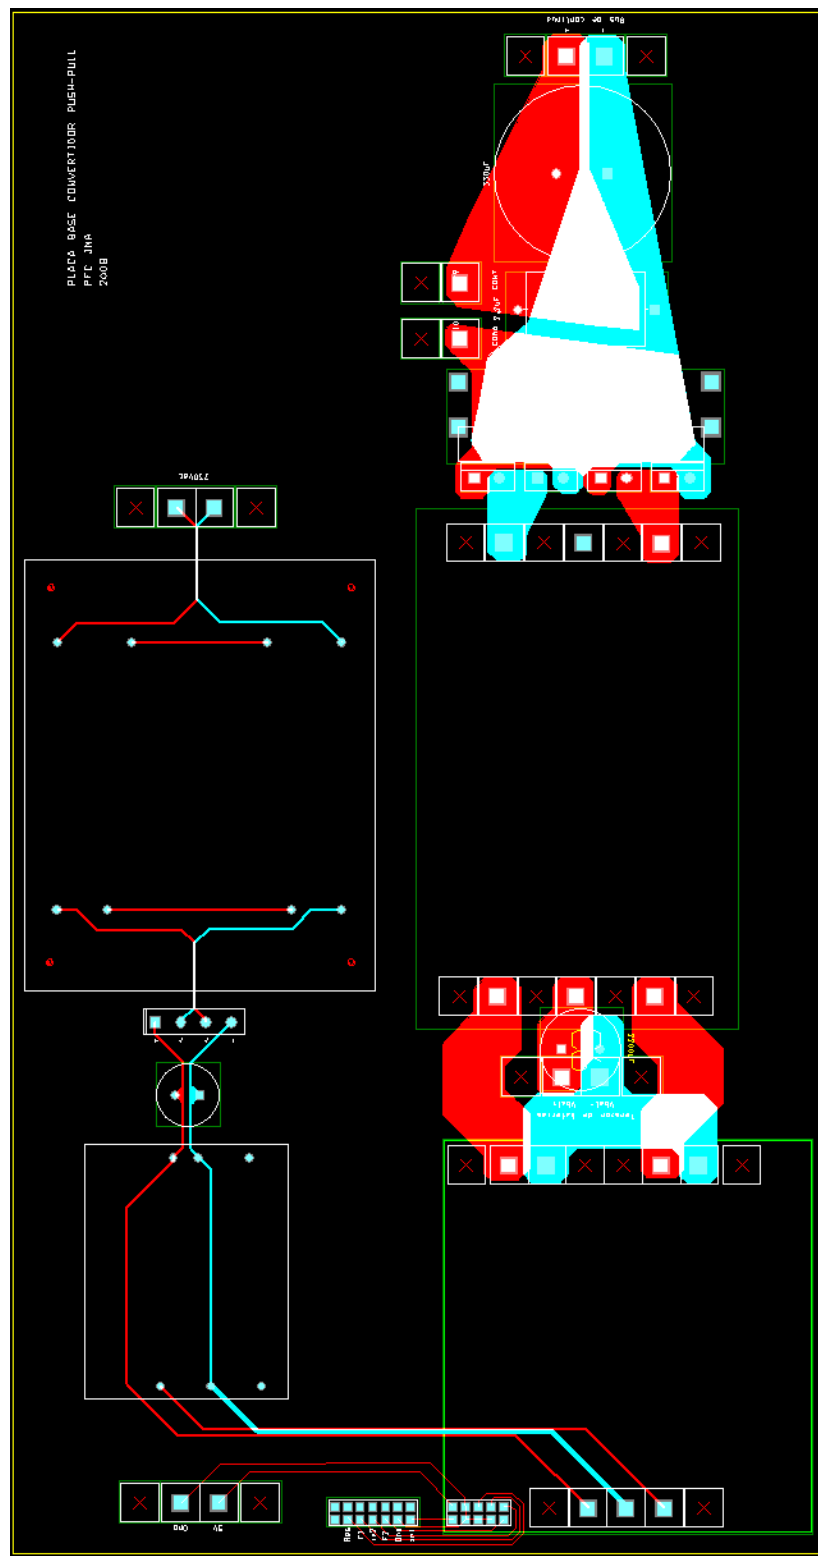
Layout de la placa base Push-Pull (31cm x 16,1cm)
